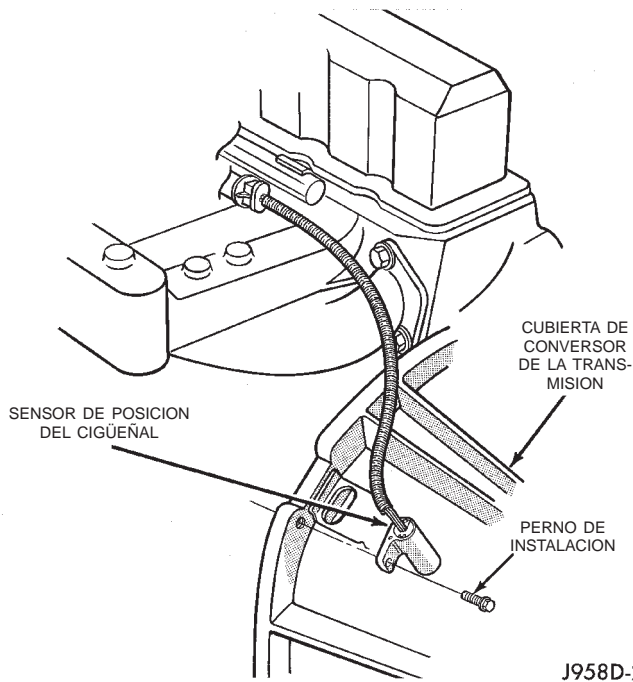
Sensor de posición del cigüeñal—Motor 4.0L
